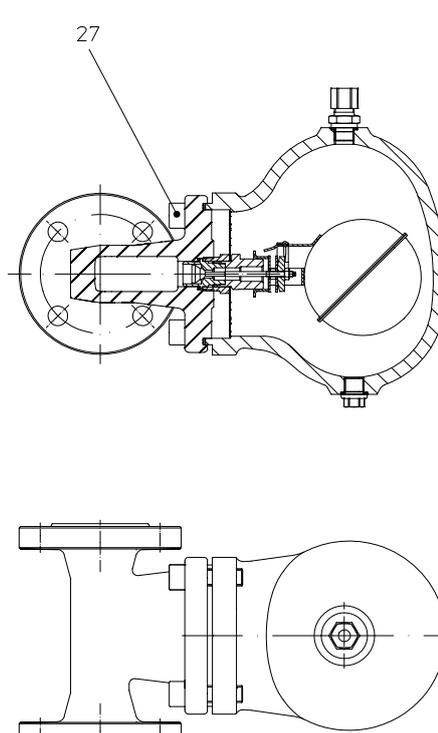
1 mit Flanschen - horizontale Einbaulage
